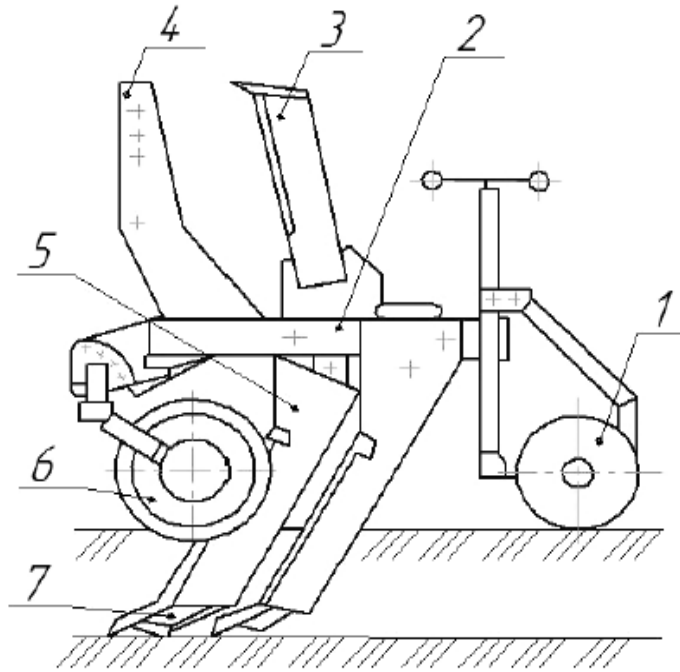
Робочий орган для безполицевого поярусного смугового обробітку ґрунту: 1 - коток прикочувальний, 2 - навішування триточкове, 3 - рама навісна, 4 - механізм регулювання глибини обробітку, 5 - стрілочаста лапа, 6 - робочі органи другого ярусу, робочі органи третього ярусу, 7 - змінне долото.
